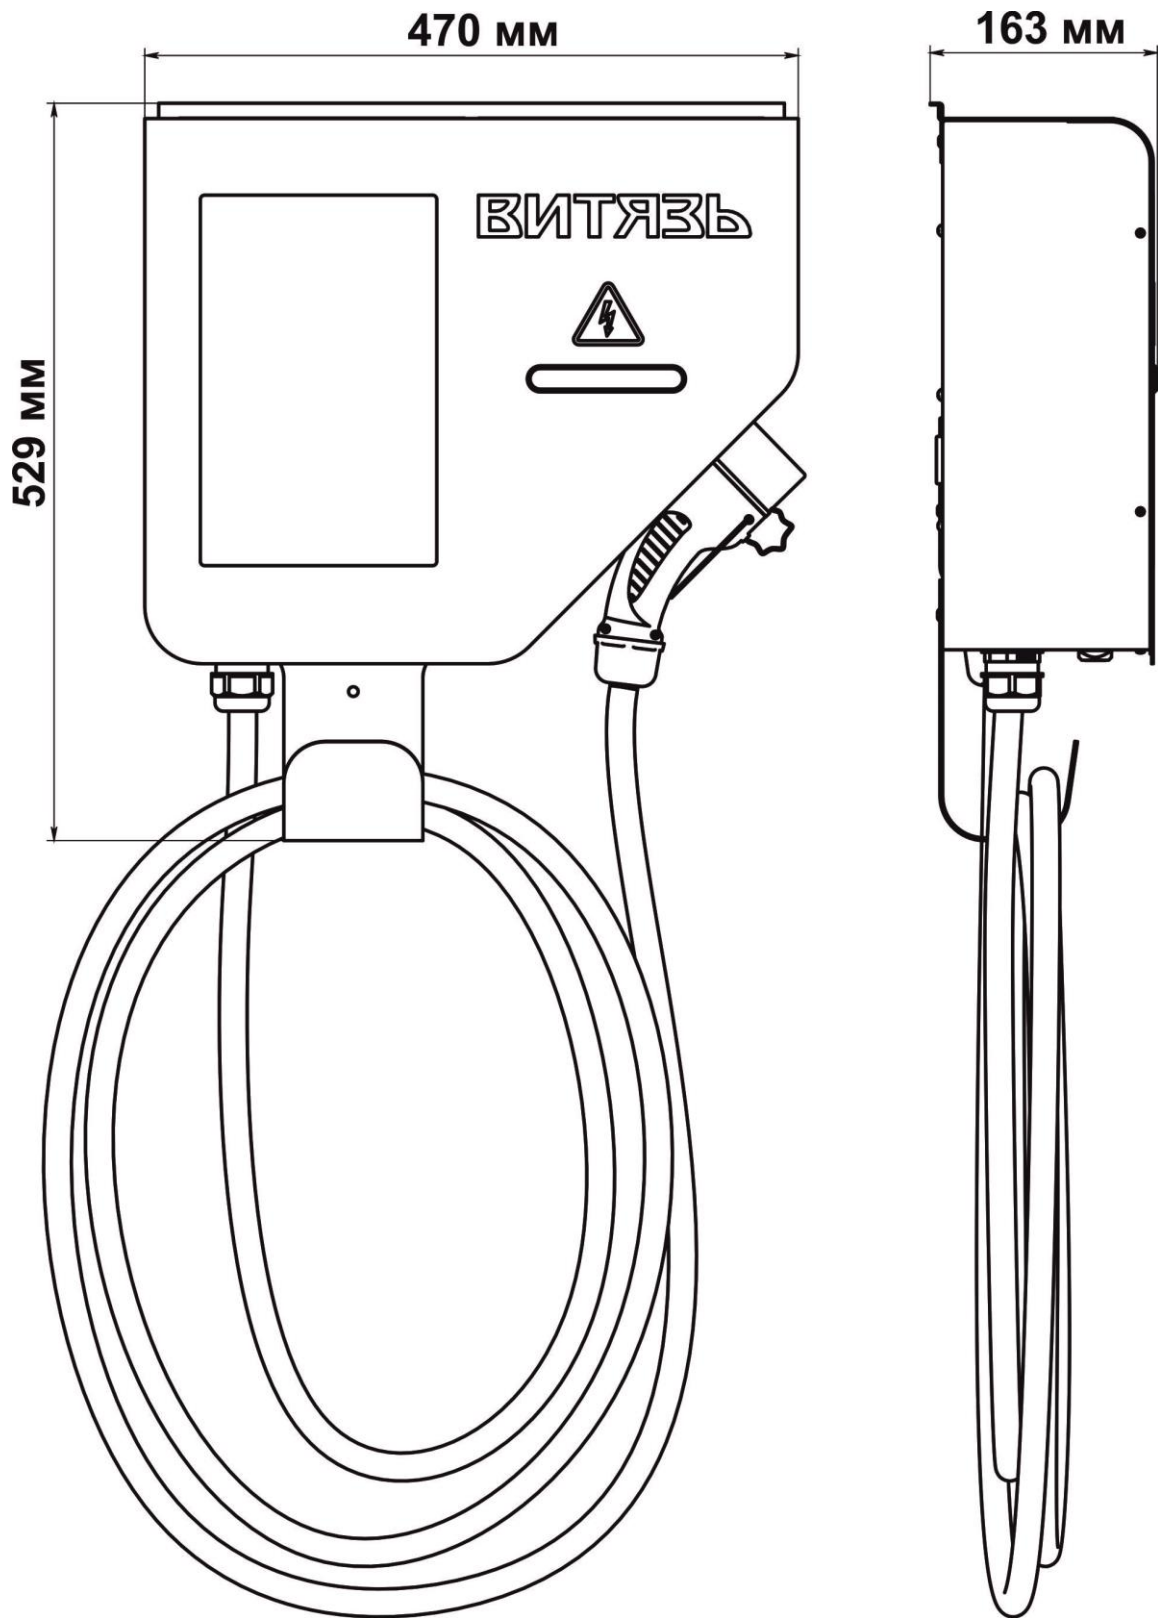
Габаритный чертеж станций ЕС-302-28, ЕС-302-38
